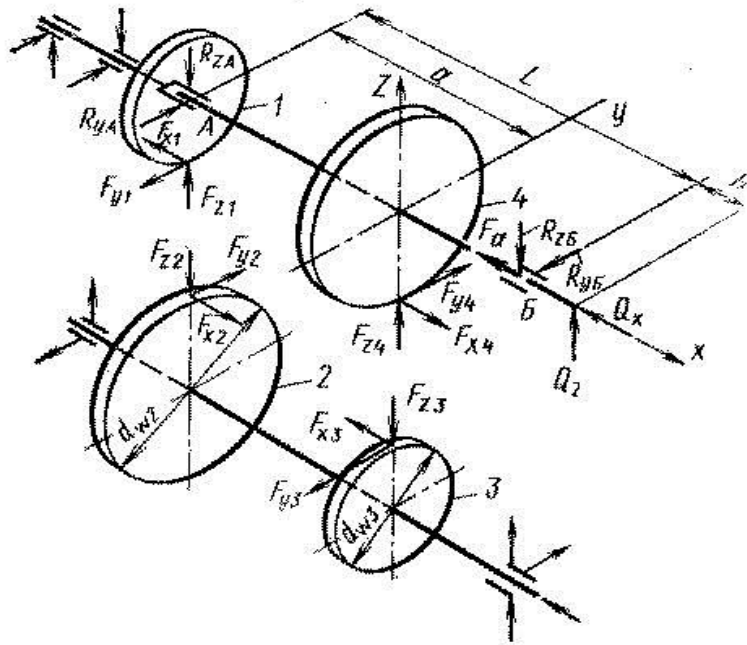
Расчетная схема сил, действующих на зубчатые колеса и подшипники передач.
